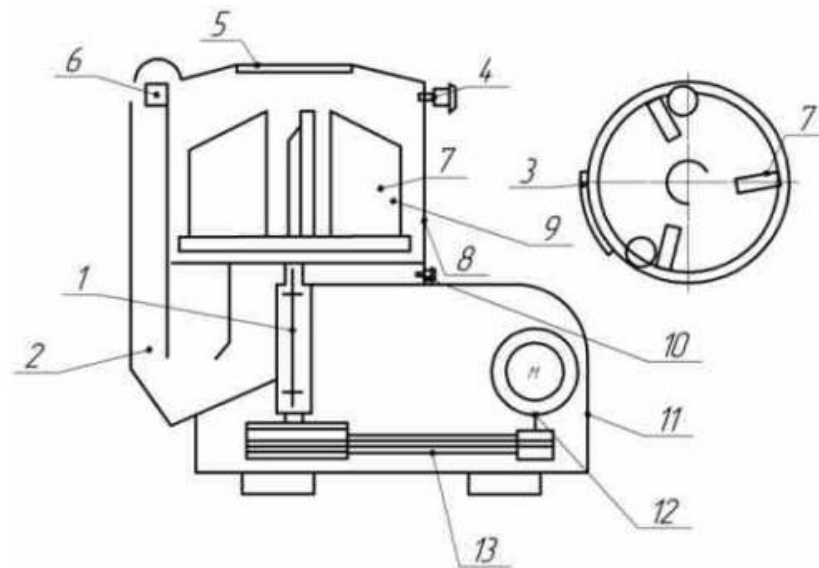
Принципова схема роторної овочерізальної машини МРО 400-1000
